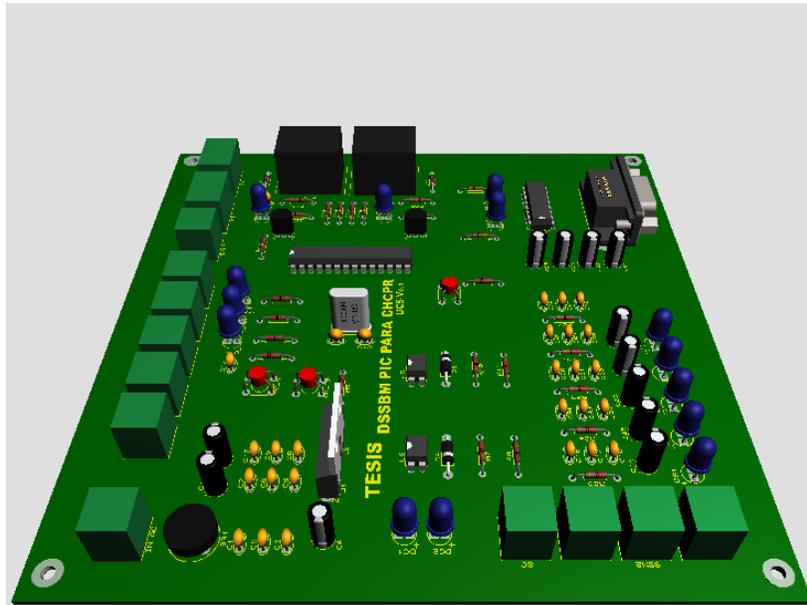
Tarjeta en 3D, vista izquierda (Proteus)
